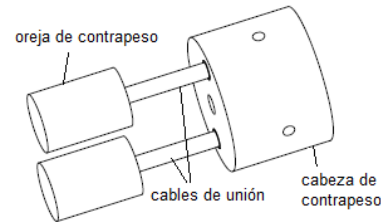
Esquema de contrapeso montado en estructura metálica.
